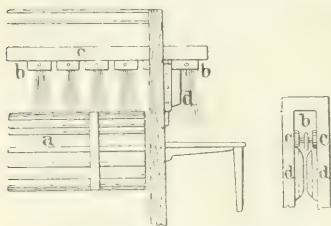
Hechelmaschine mit Schutzvorrichtung von Schöller, Bückler & Co.
